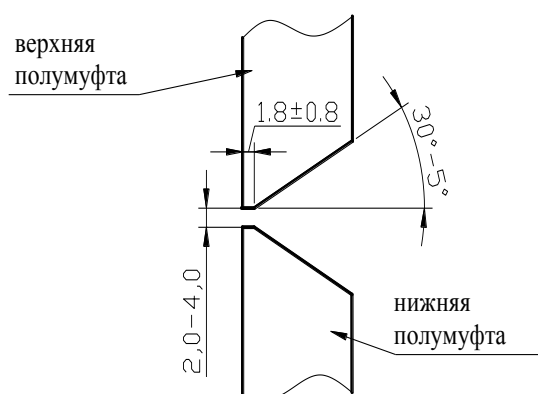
Форма разделки кромок продольного стыка муфты при ремонтной сварке нефтепровода
